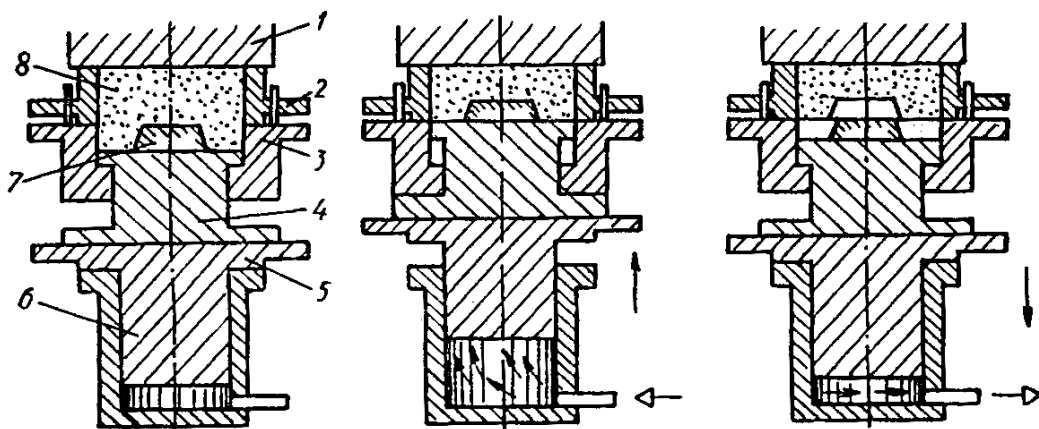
Схема формувальної машини: 1 — плунжер; 2 — опока; 3 — стіл; 4 — плита модельна; 5 — корпус; 6 — поршень; 7 — модель
